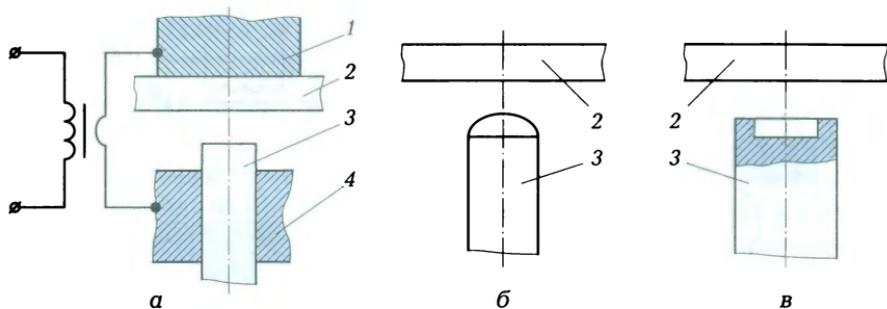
Схемы Т-образной сварки листа с плоским (а), сферическим (б) и с отверстиями (в) торцами стержней:
